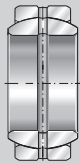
· Unrundheit vor, Rundheit nach dem Einbau
